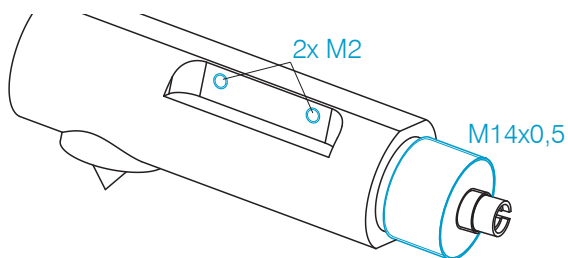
Montage für Sensoren der Serie IFS2407/90-0,3
